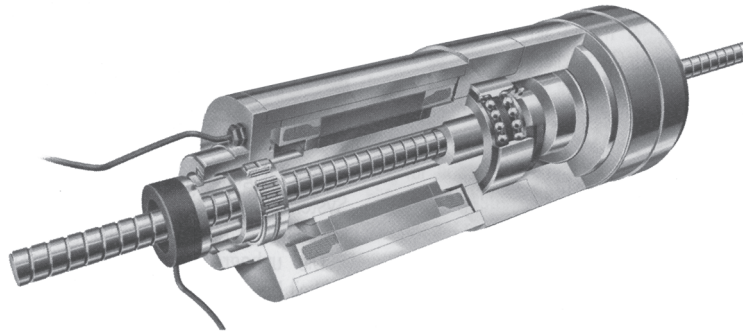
Beispiel: Spindel-Mutter-System mit angetriebener Wälzschraubmutter und Hohlwellenmotor [INA-SCHAEFFLER KG; 60]
